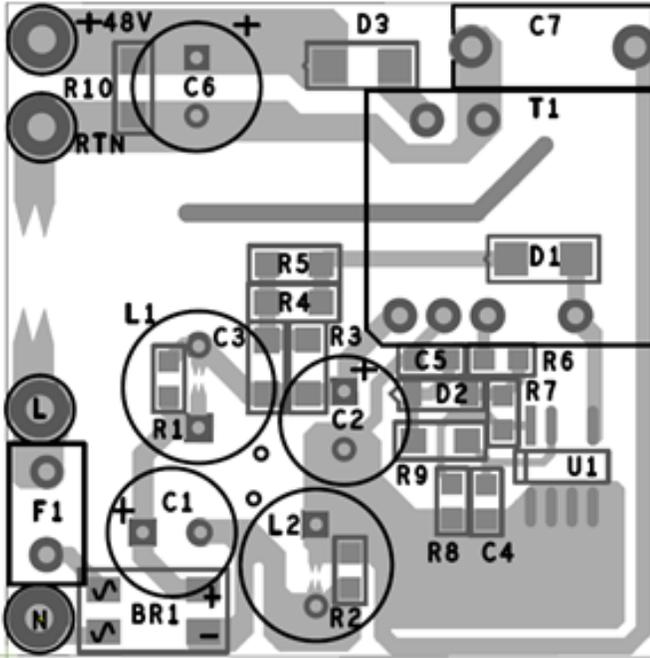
SO-8C 패키지를 사용하는 PCB 레이아웃 예
